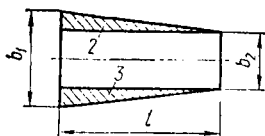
Схема фрезерования конических зубчатых колес с прямым зубом
